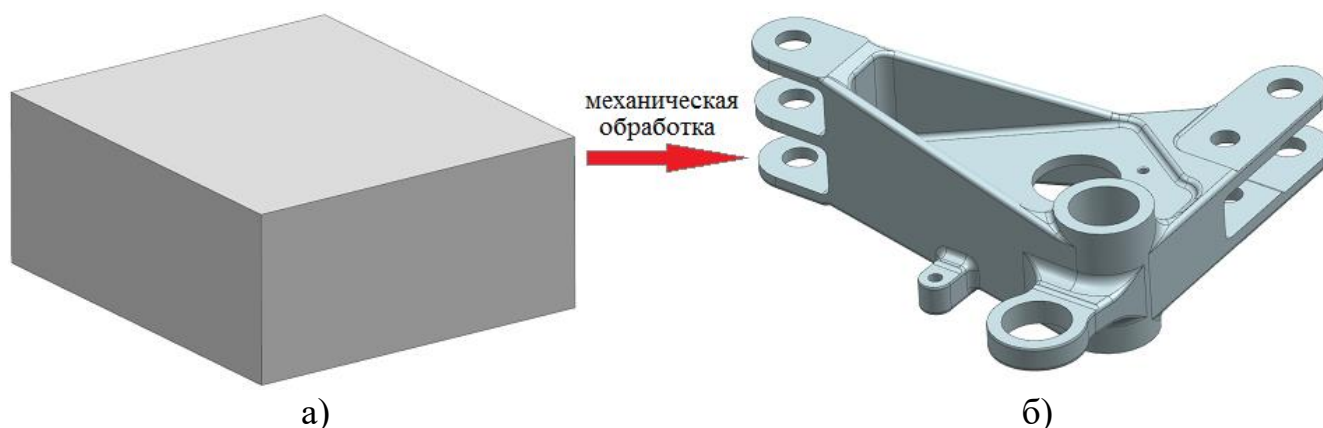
Заготовка (а) из алюминиевого сплава АК6 (габарит 180×160×80 мм) и деталь «Качалка» (б) механизма управления вертолетом
